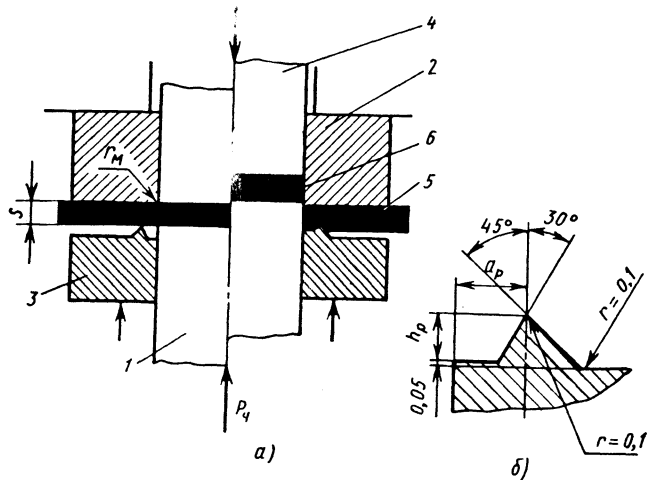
Схема чистой вырубки-пробивки со сжатием прижимом с клиновидным выступом (а) и профиль зуба (б): 1 - пуансон; 2 - матрица; 3 - прижим с клиновидным выступом (зубом); 4 - контрпуансон; 5 - заготовка; 6 - деталь
